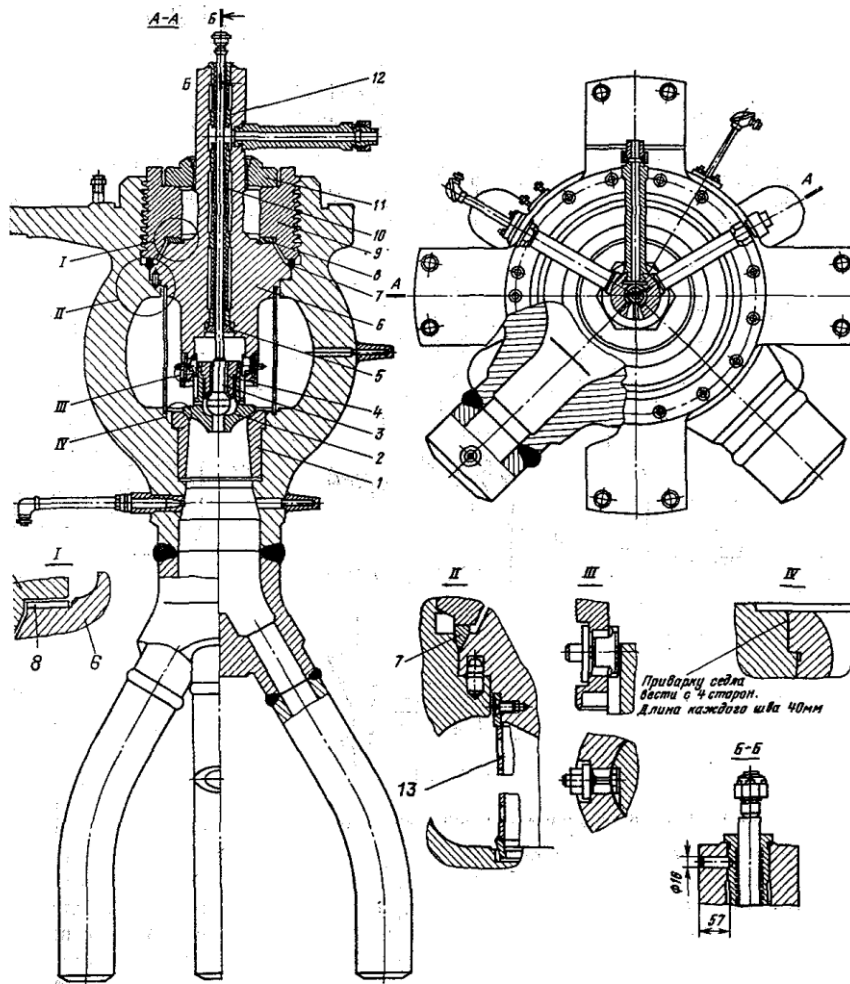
Стопорний клапан турбіни К-300-240:
